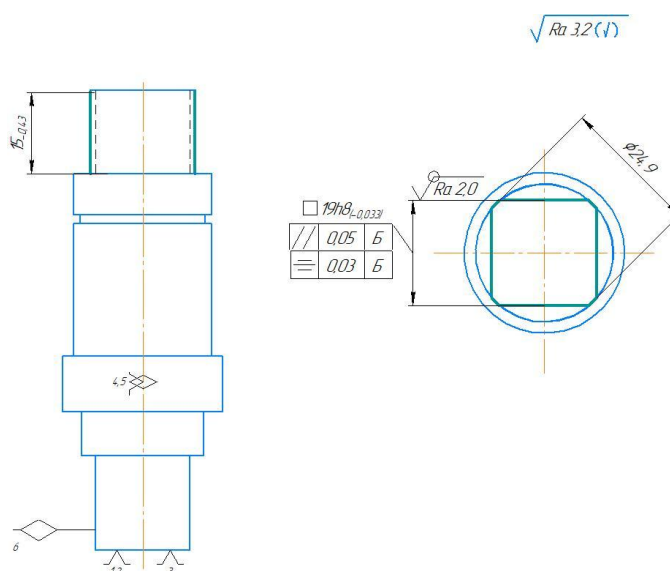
схема установки заготовки в приспособление(Установ А).
